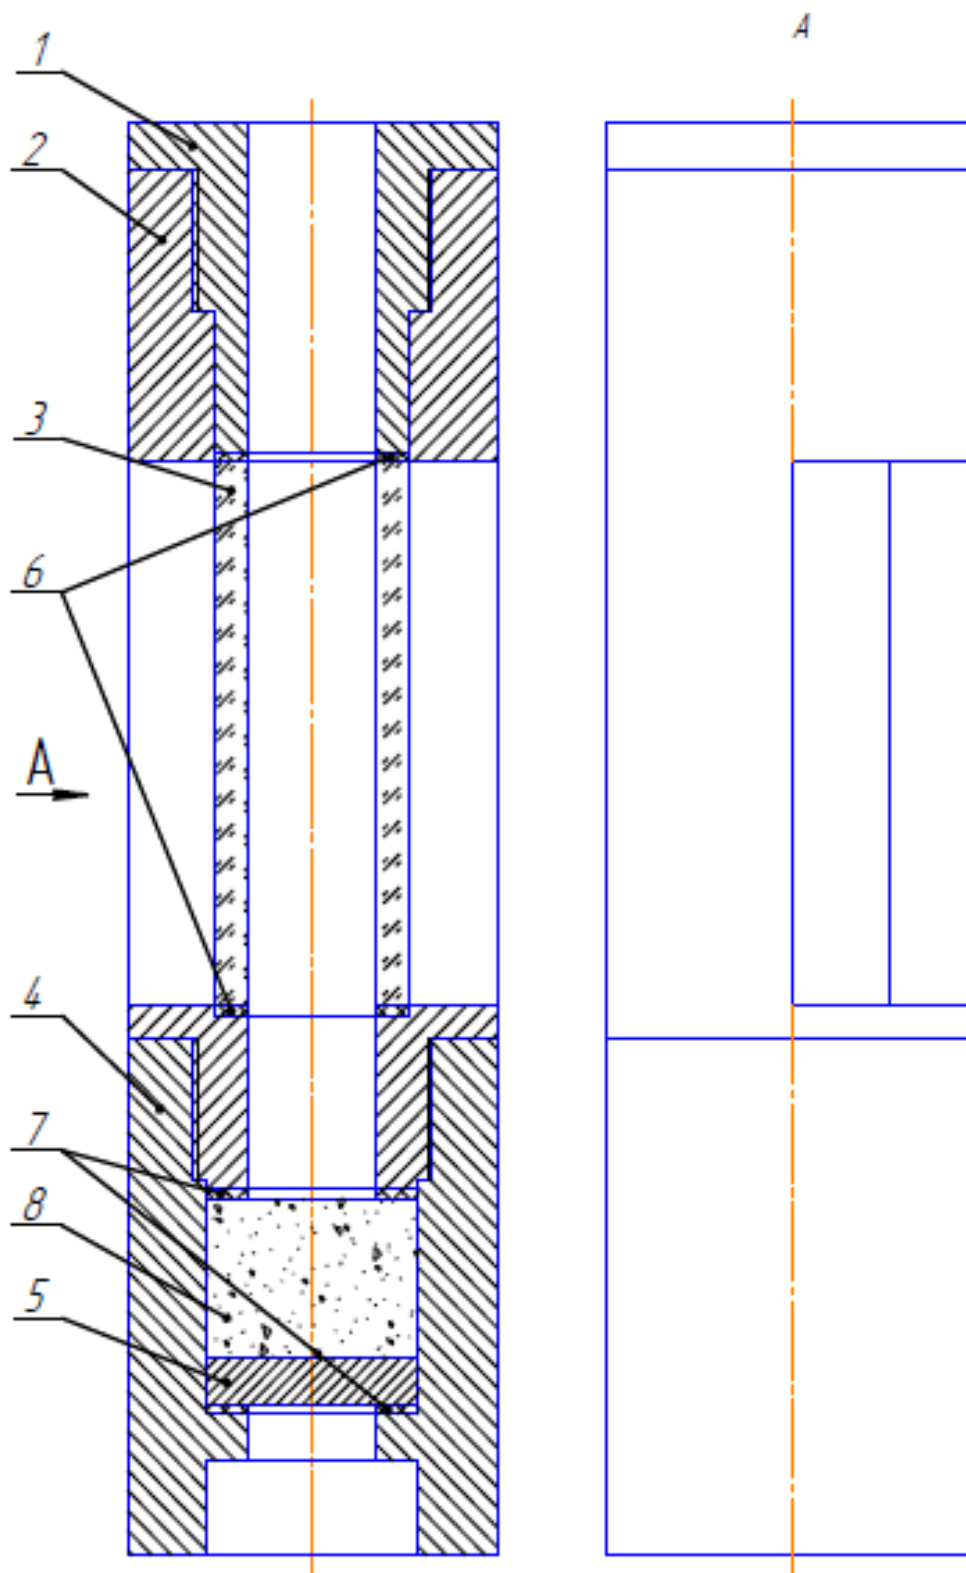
Стакан для размещения образца разрушаемого материала: 1 – верхний нажимной цилиндр стакана; 2 – средний цилиндр стакана; 3 – прозрачная труба; 4 – нижний цилиндр стакана; 5 – опорный диск; 6, 7 – резиновая прокладка; 8 – образец разрушаемого материала.
